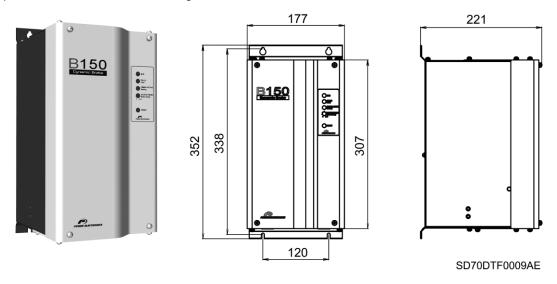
Módulo de frenagem dinâmica B150. Dimensões [mm]
